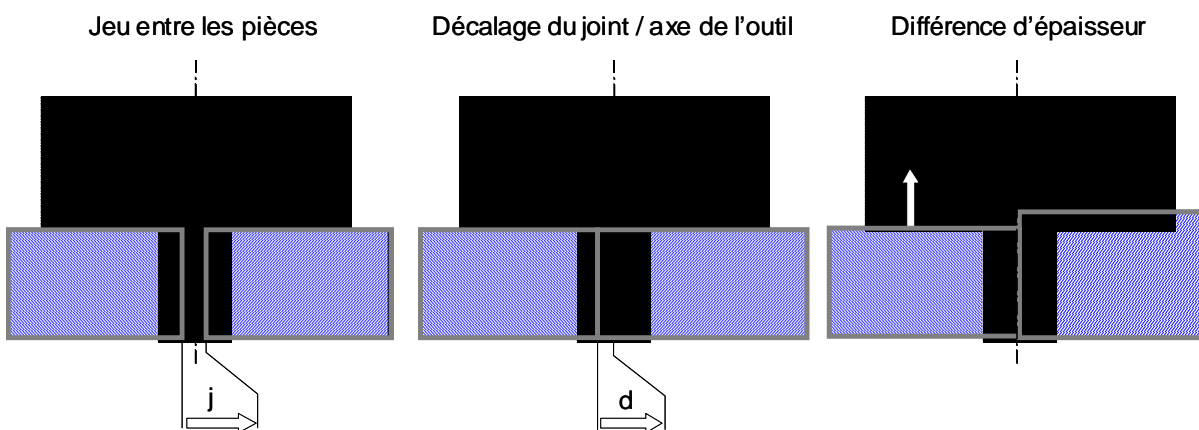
défaut de préparation des pièces et défaut de suivi de trajectoire
